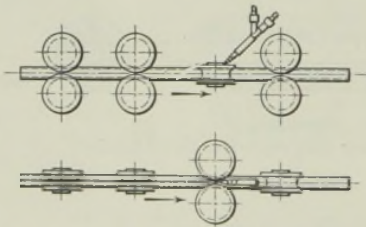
Schweißen des Rohres in der Gasschmelz-Rohrschweißmaschine.
